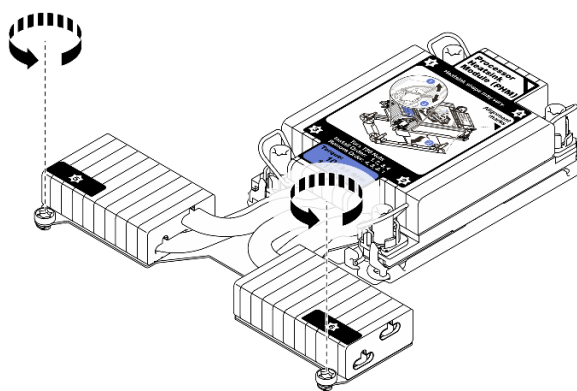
Desserrage des vis du dissipateur thermique en forme de T
